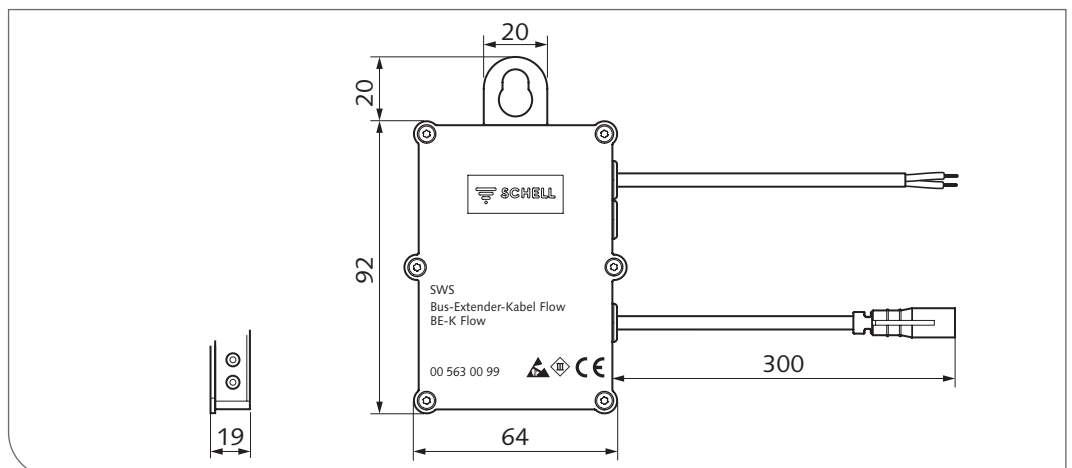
Extensor de bus SWS por cable Flow BE-K Flow. Dimensiones
